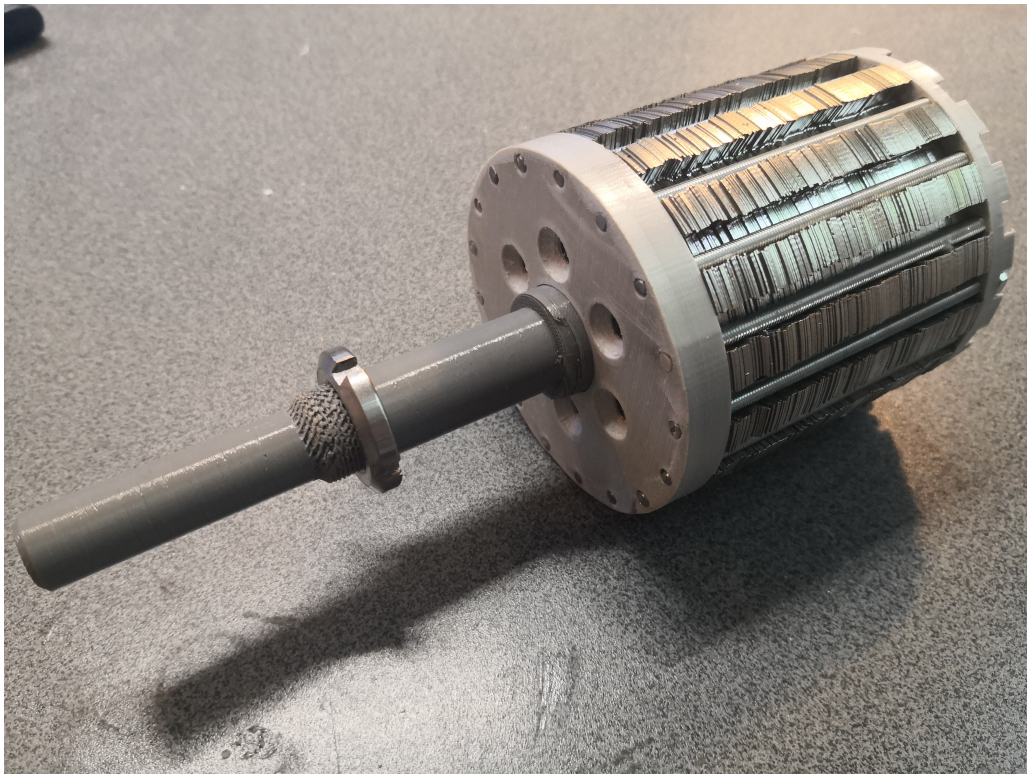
Rotor basse vitesse, pièces polaires
